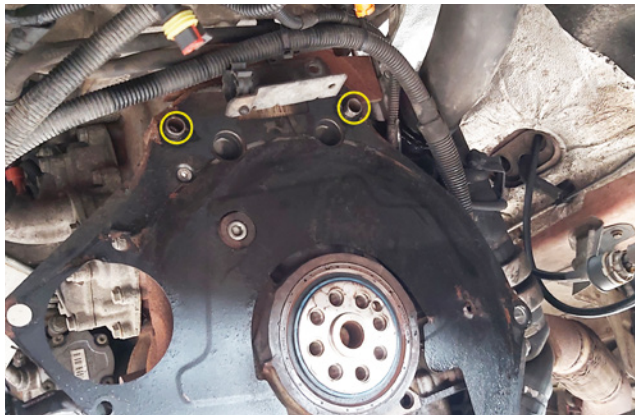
Einbaulage der Passhülsen im Zylinderblock
